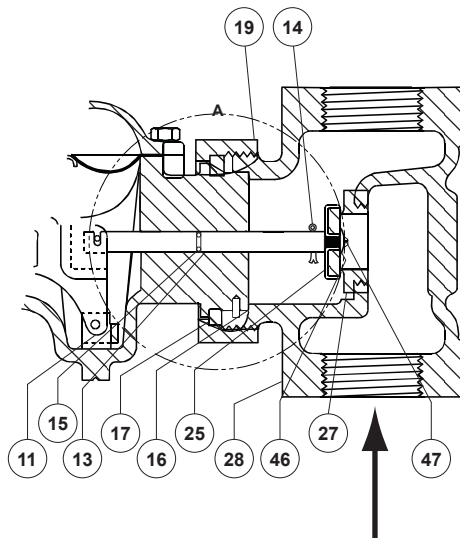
Detail der O-Ring-Schaltwellendichtung, Ausführung Y692VBM
